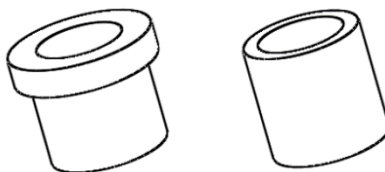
Buje modificado. Izquierda: buje original.
